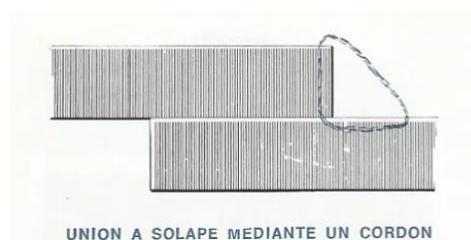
Representación de soldadura a solape [Técnica y Práctica de la Soldadura - Giachino, J.W]
